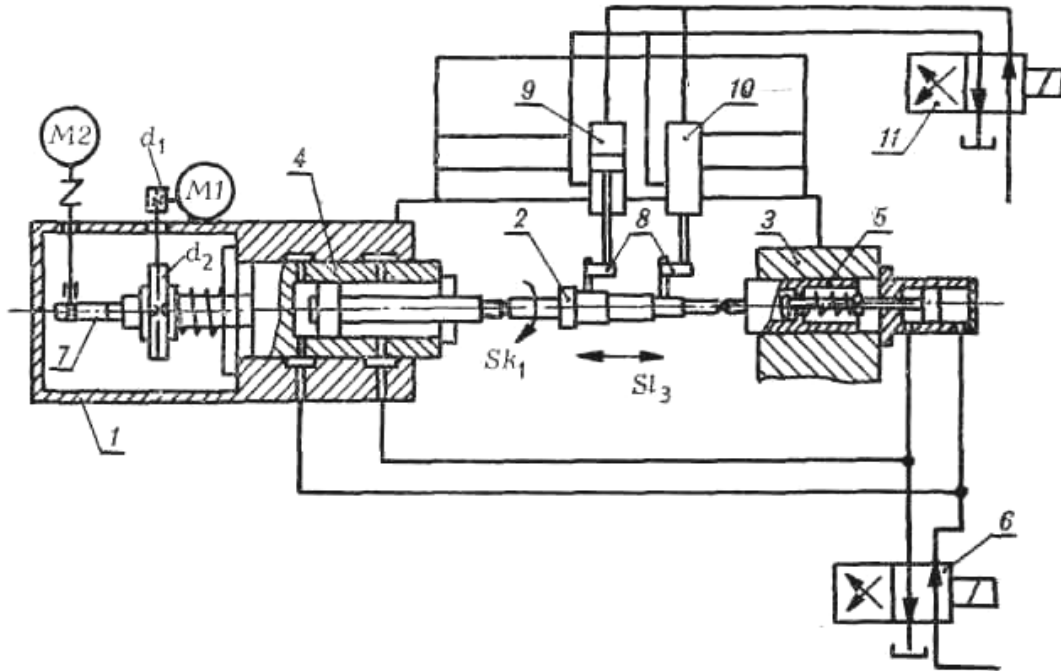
Установка для суперфиниширования цилиндрических поверхностей
